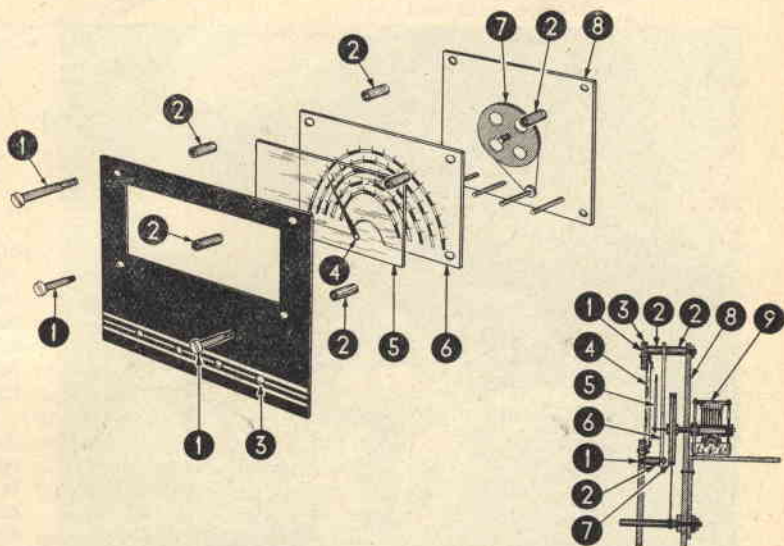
Montaggio del sovrappannello. 1 - vite; 2 - tubetto distanziale; 3 - sovrappannello; 4 - lancetta quadrante; 5 - vetro copertura quadrante; 6 - quadrante su cartoncino; 7 - demoltiplica e funicella; 8 - pannello frontale del telaio; 9 - condensatore variabile.
